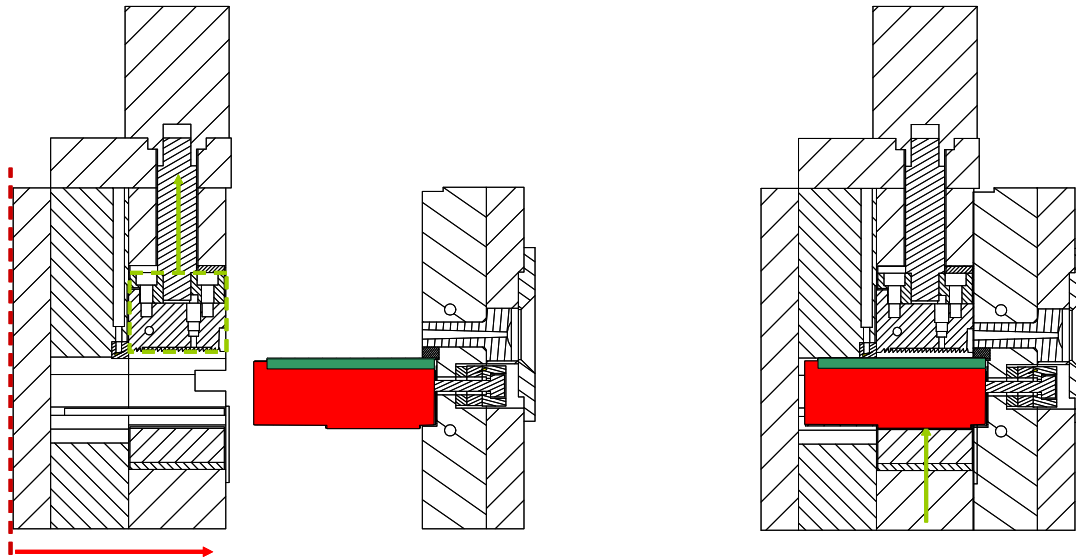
Versuchsablauf, Werkzeugschließvorgang und Abdichten des Werkzeuges [12].
